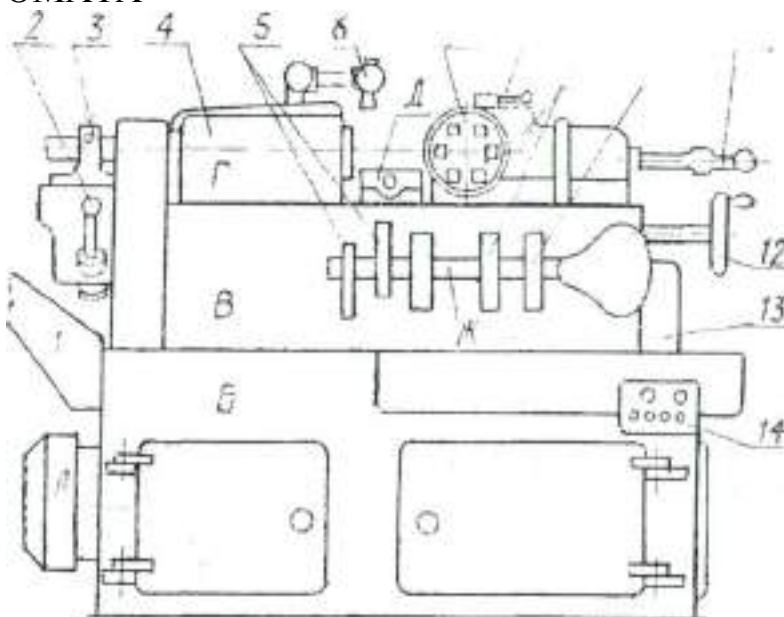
ОБЩИЙ ВИД АВТОМАТА
